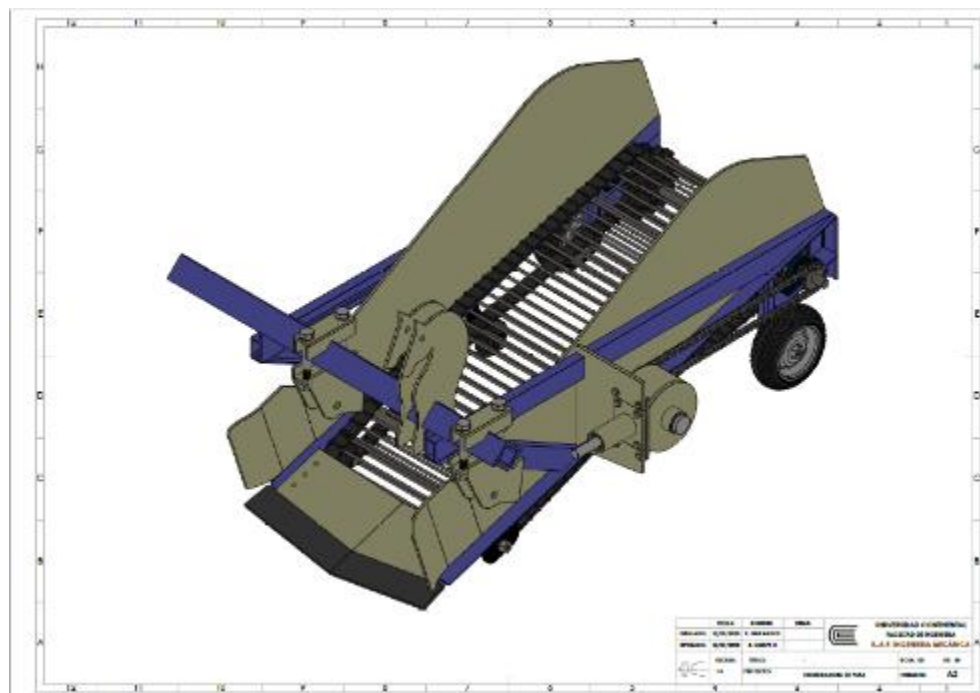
Diseño definitivo de la maquina cosechadora.
